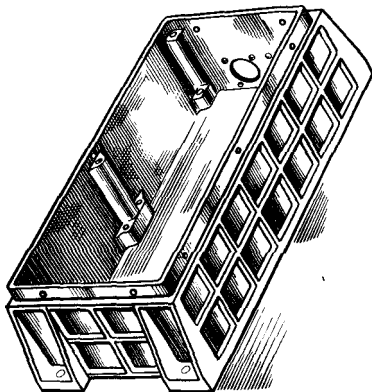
Корпус бортового РЭС, фрезерованный из слитка (поковки)
